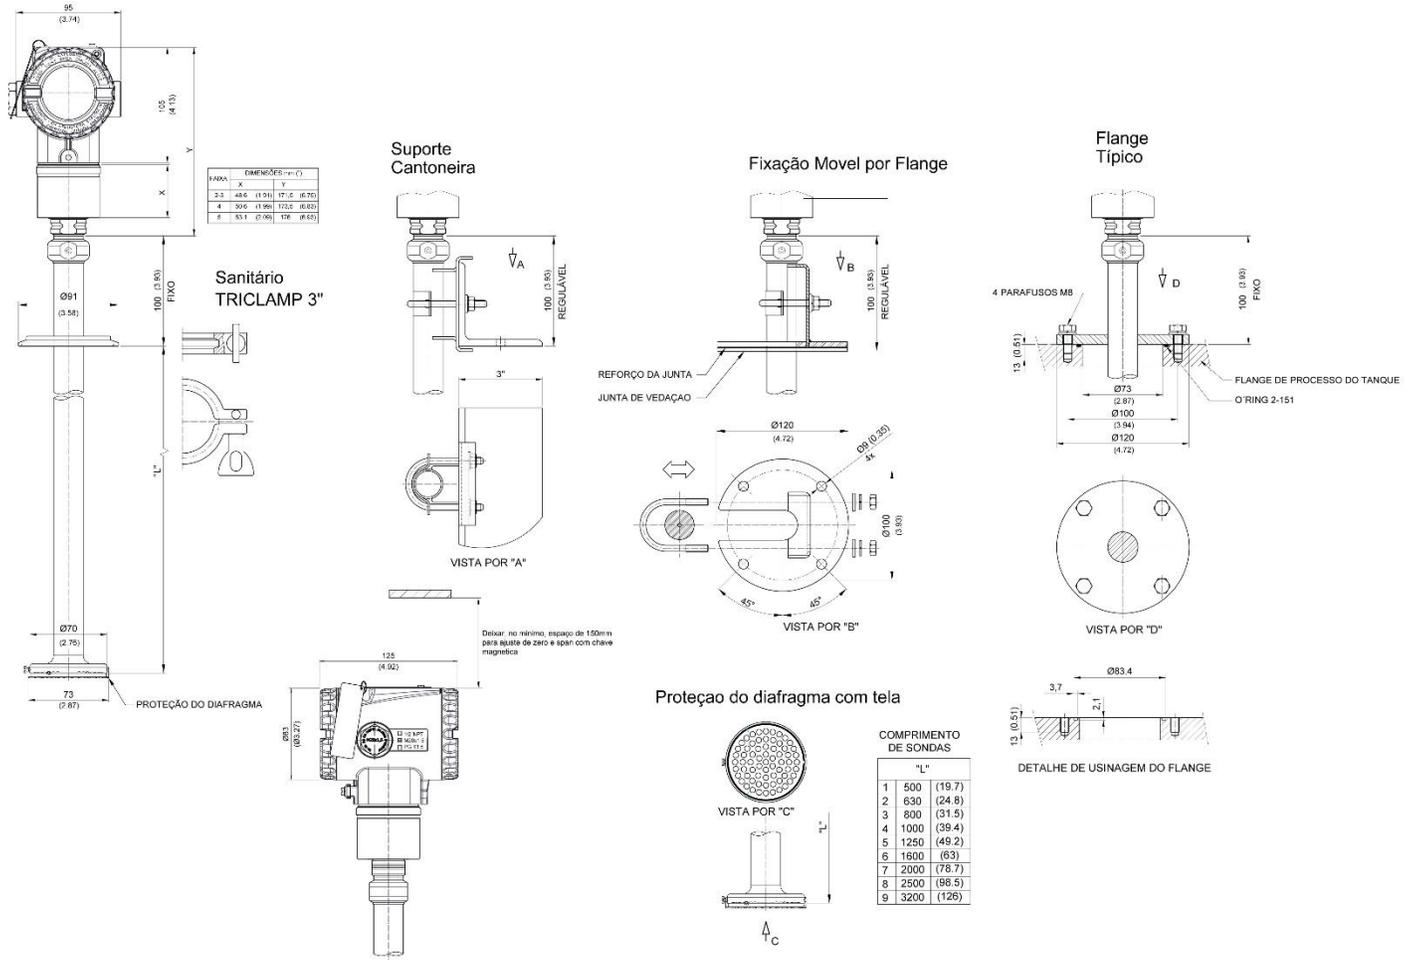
(f) – Desenho Dimensional de Montagem do LD400 HART - Transmissor de Pressão com Haste de Inserção
